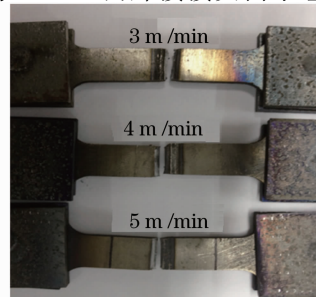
22MnB5 焊接接头拉伸断裂试样
